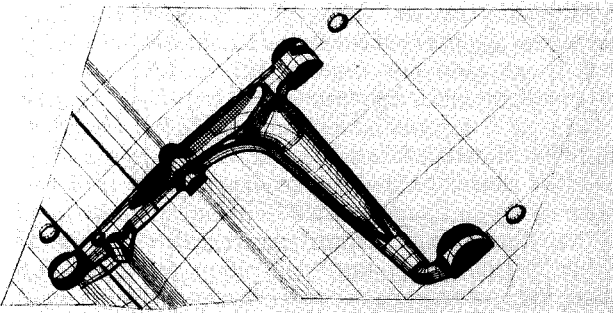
Querlenker; CAD-Geometrie für Fertigpreßgesenk
